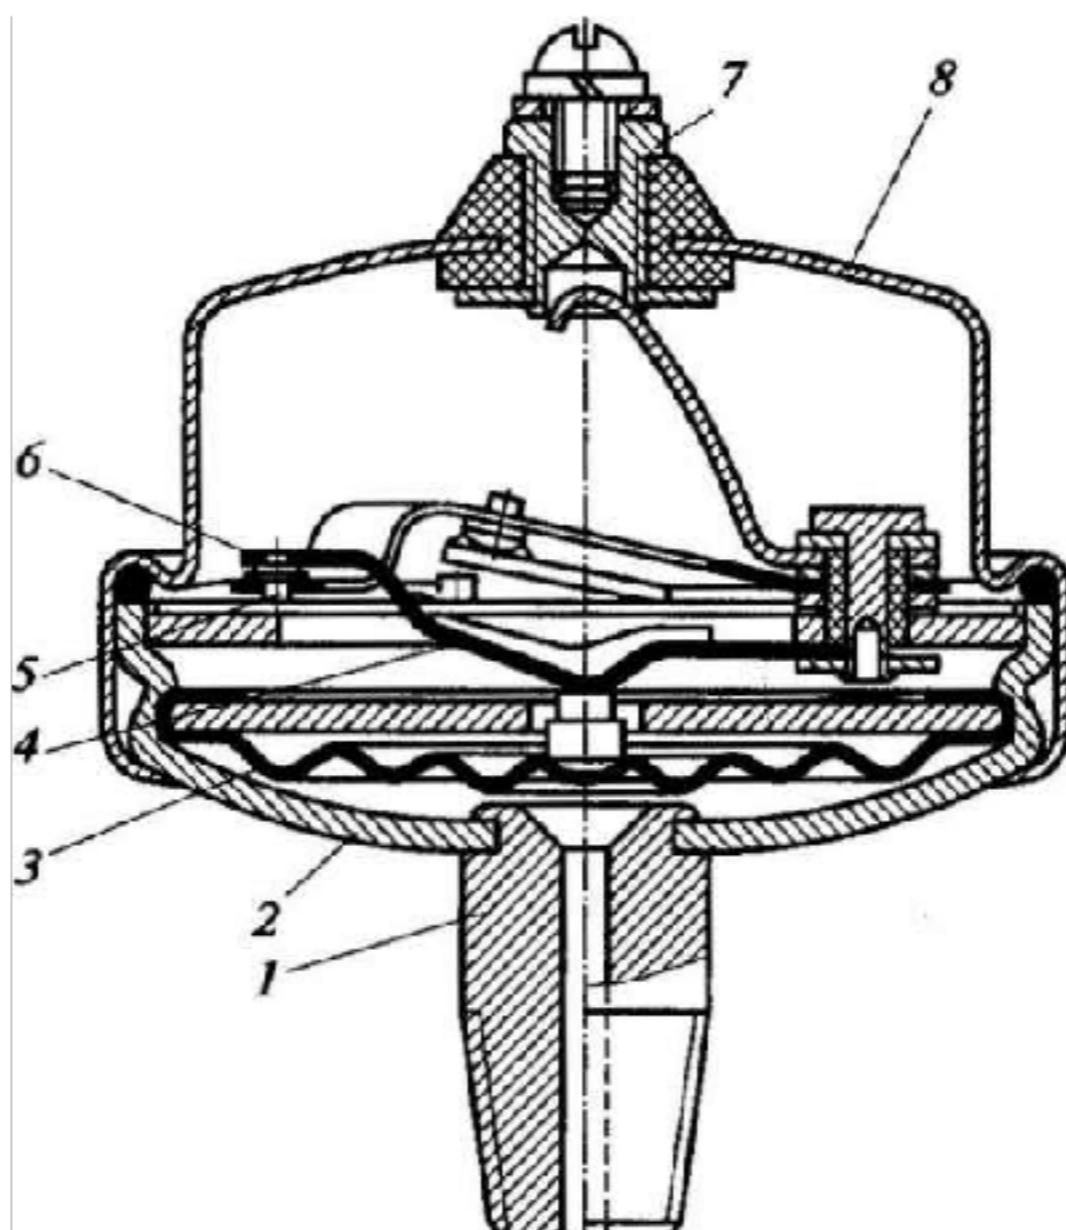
Мембранный датчик аварийного давления масла: 1 — штуцер; 2 — корпус; 3 — мембрана; 4 — рычаг выключателя; 5 — неподвижный контакт; 6 — подвижный контакт; 7 — выводной контакт; 8 — кожух
